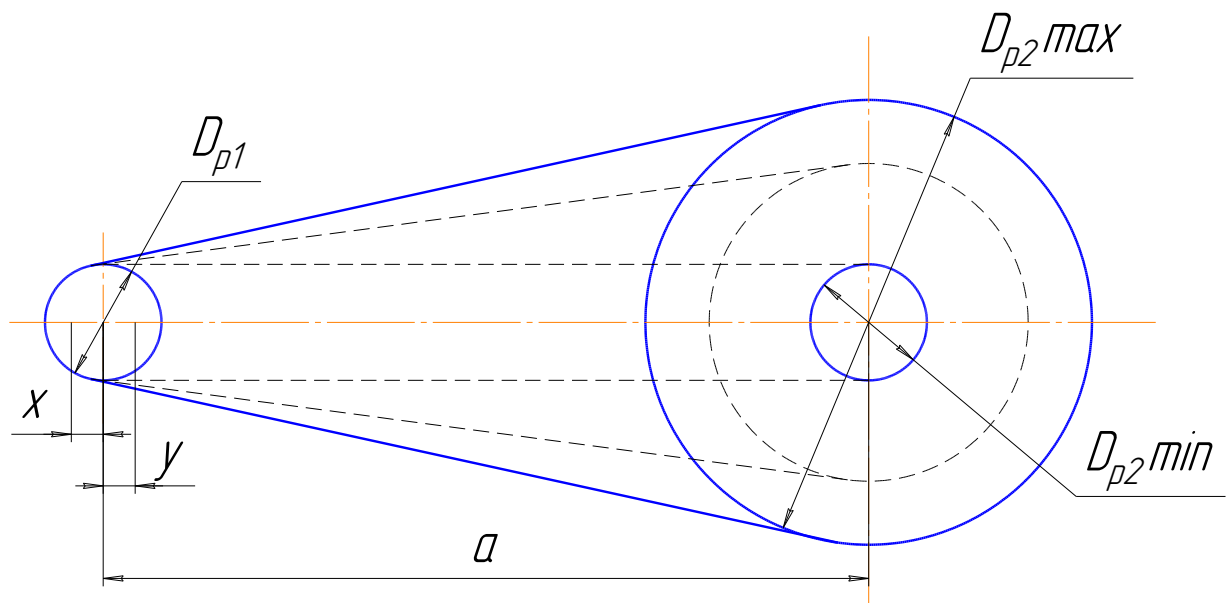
Розрахункова схема механічного клинопасового варіатора механізму приводу
